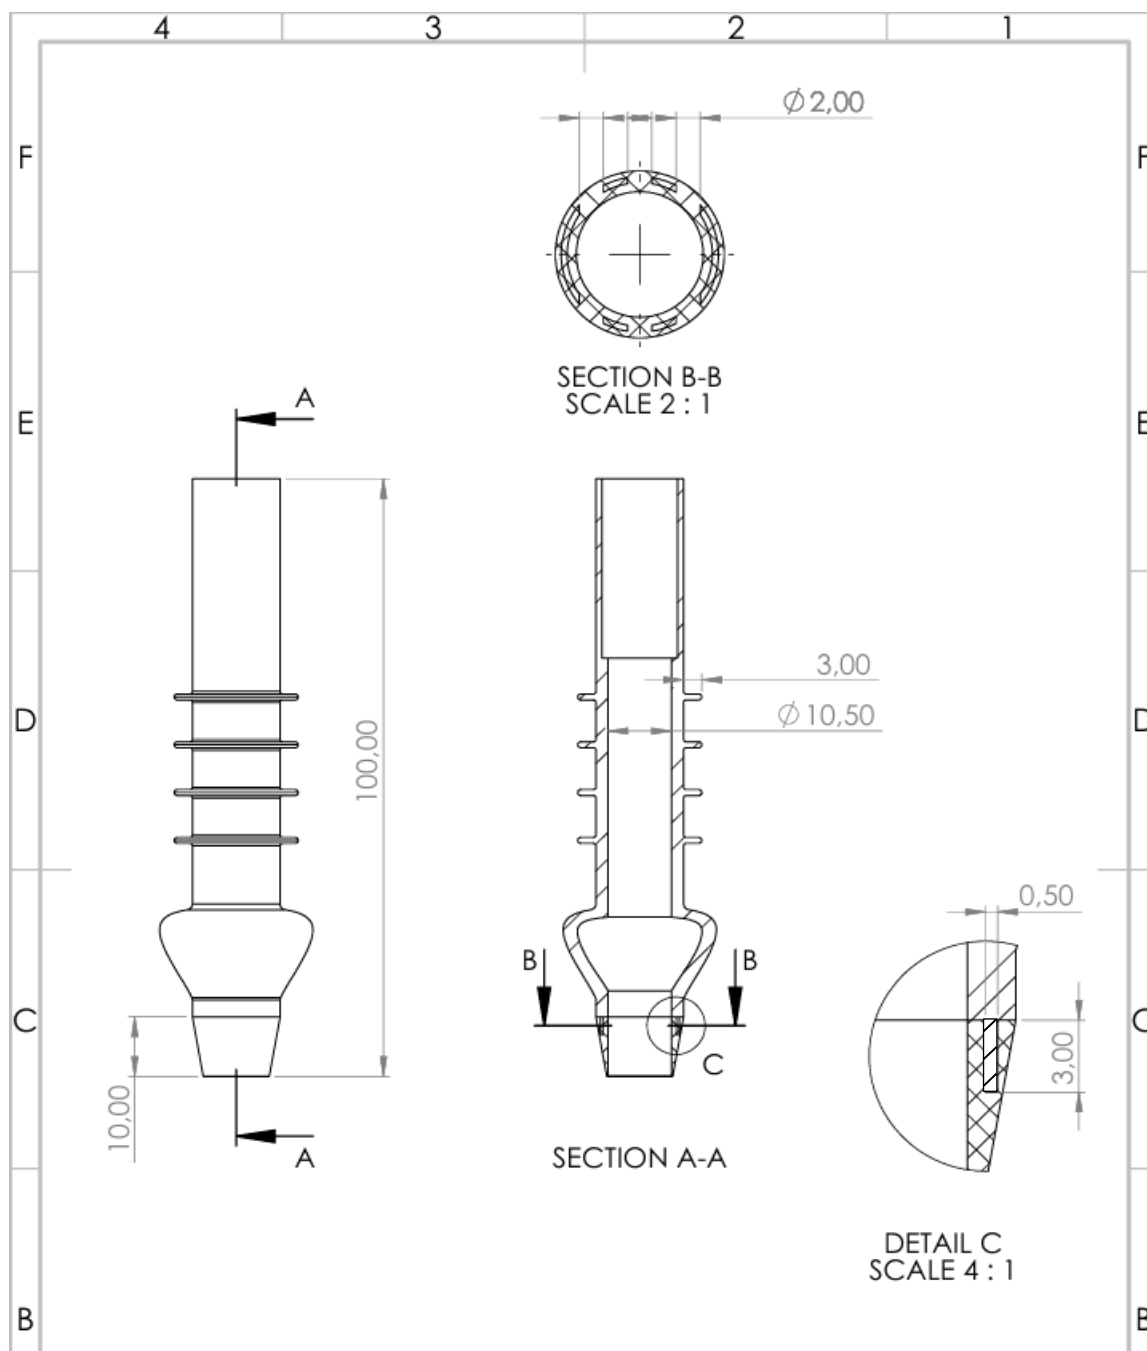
Desenho técnico da cânula desenvolvida com dimensões importantes detalhadas.
